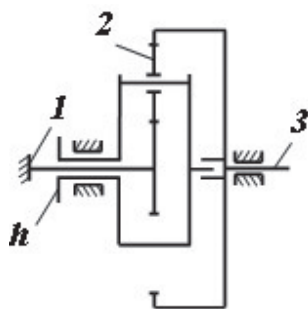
Схема планетарной передачи: 1 — малое центральное колесо; 2 — сателлит; 3 — большое центральное колесо; 4 — водило
